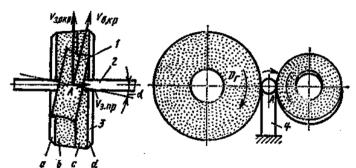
Схема обработки на бесцентрово-шлифовальном станке
